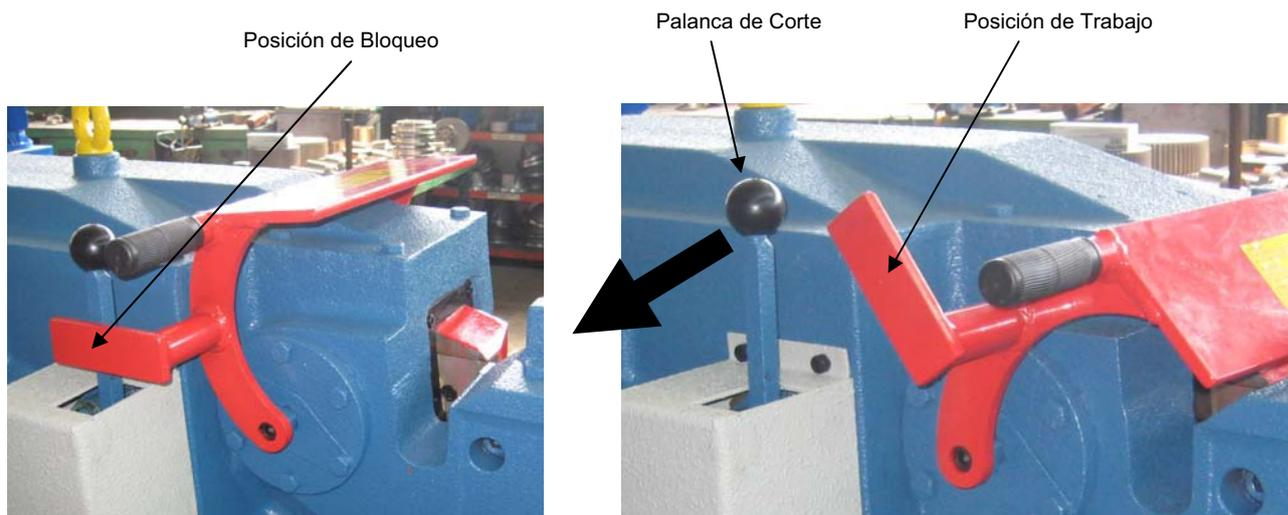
Palanca de Corte bloqueada (izquierda) y desbloqueada (derecha)
